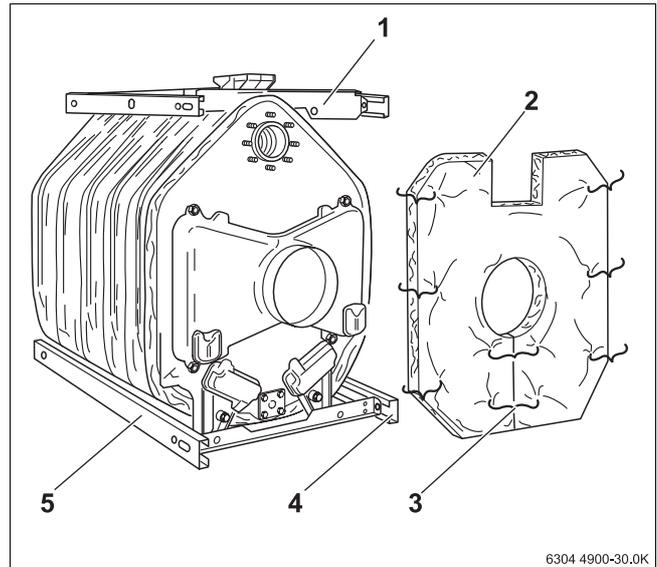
Montaggio delle traverse longitudinali inferiori e dell'isolamento termico
